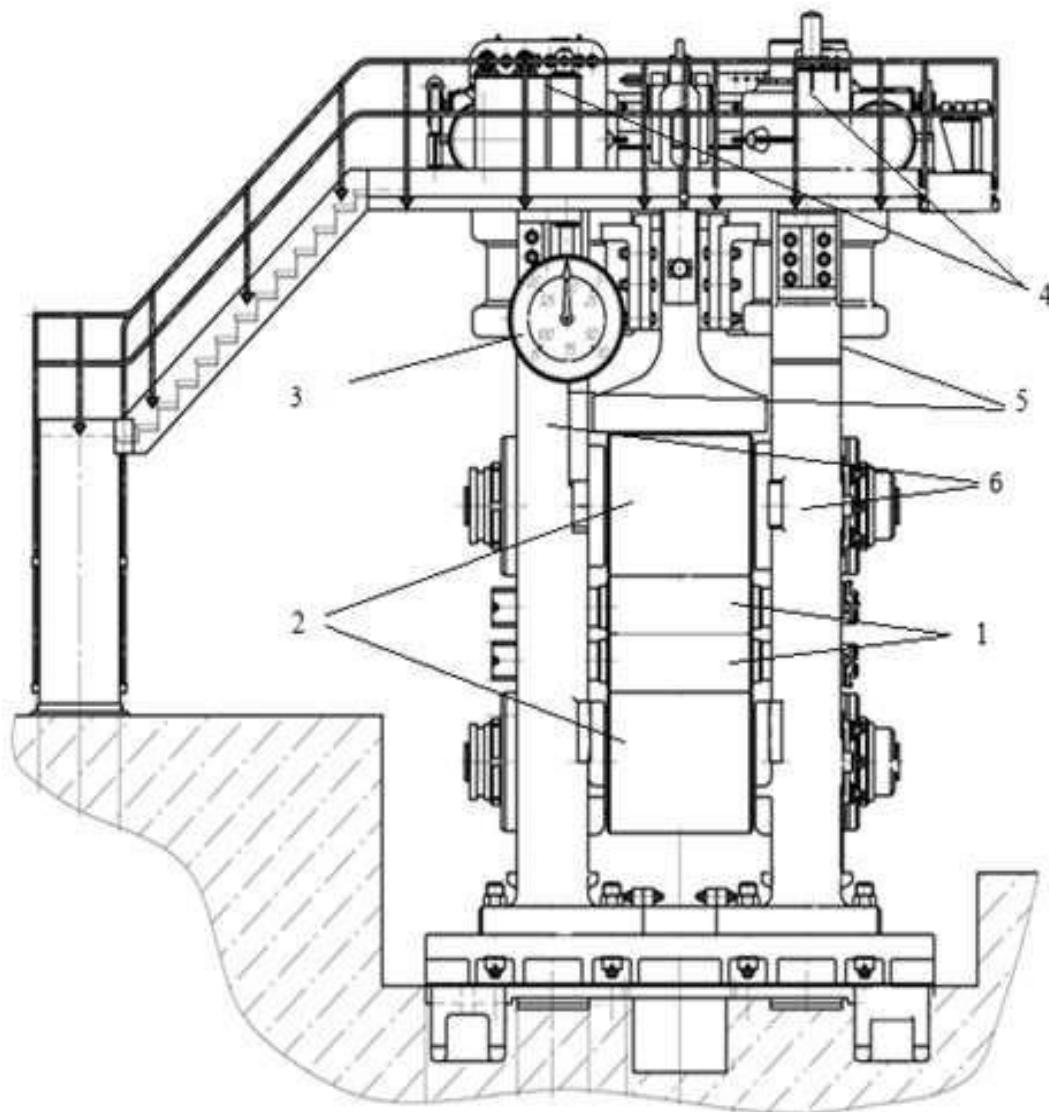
Общий вид реверсивного стана «Кварто 1500»
